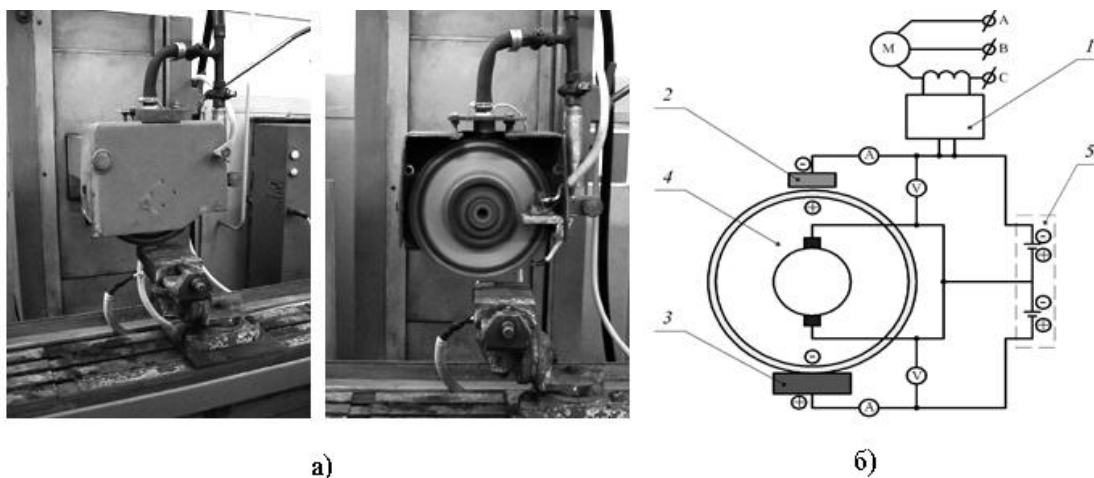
Общий вид модернизированных узлов станка 3E711 (а) и схема процесса комбинированной обработки (б)
